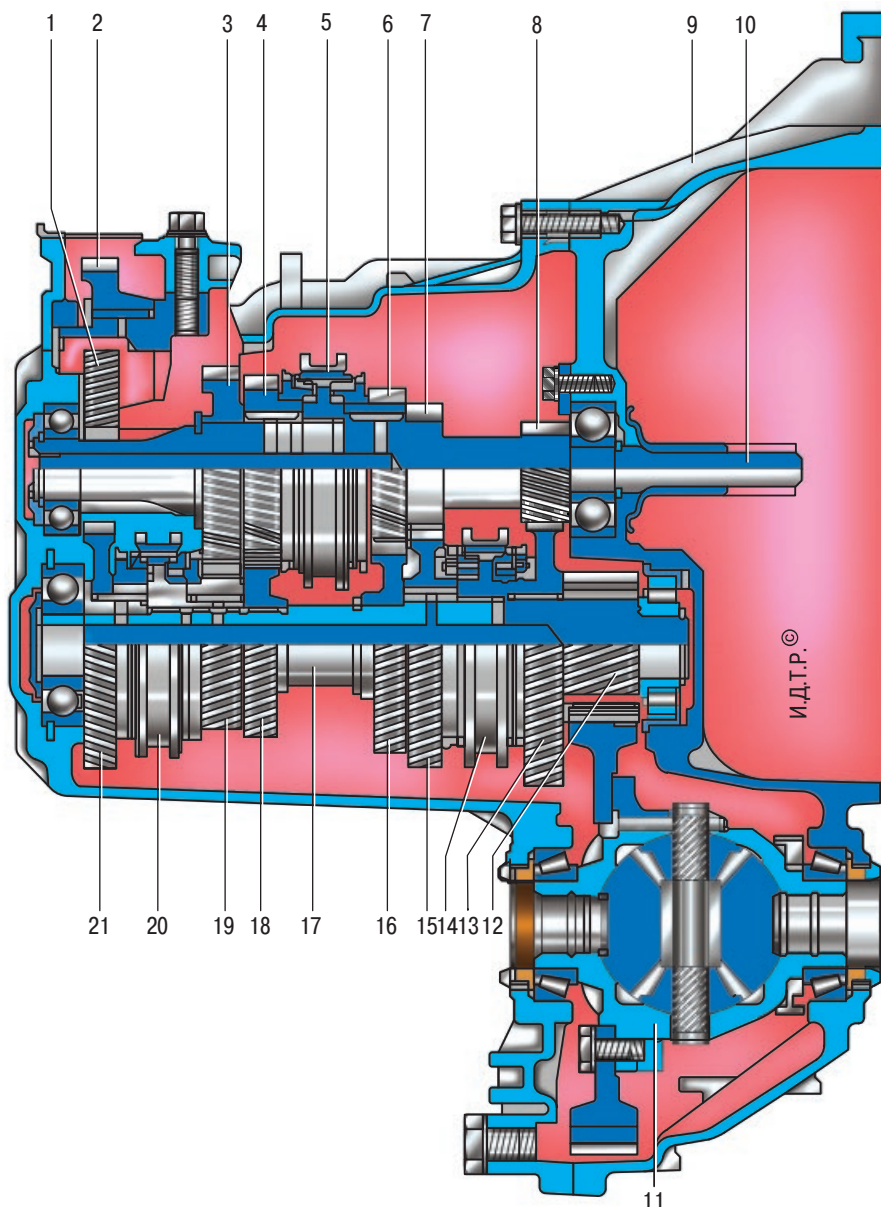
Принципиальная схема шестиступенчатой механической коробки передач мод. МТХ-75: 1 – шестерня передачи заднего хода; 2 – шестерня V передачи; 3 – ведущая шестерня IV передачи; 4 – муфта включения III и IV передач; 5 – картер коробки передач; 6 – ведущая шестерня III передачи; 7 – шестерня II передачи; 8 – шестерня I передачи; 9 – картер сцепления; 10 – первичный вал; 11 – корпус дифференциала; 12 – ведущая шестерня главной передачи; 13 – ведущая шестерня I передачи; 14 – муфта включения I и II передач; 15 – ведущая шестерня II передачи; 16 – шестерня III передачи; 17 – вторичный вал; 18 – шестерня IV передачи; 19 – ведущая шестерня V передачи; 20 – муфта включения V передачи и передачи заднего хода; 21 – ведущая шестерня передачи заднего хода
